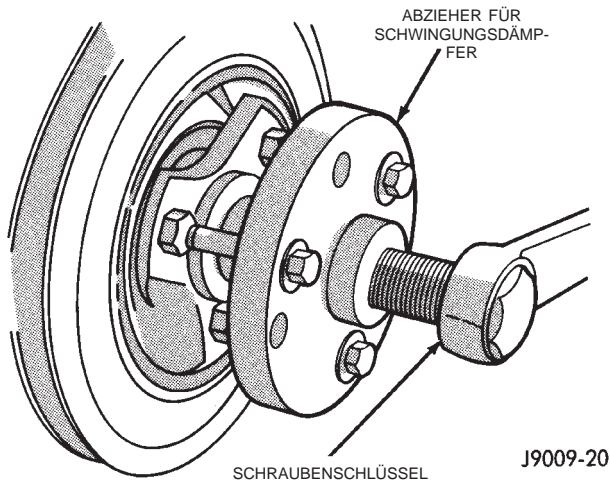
Spezialwerkzeug 7697-Abzieher für Schwingungsdämpfer
